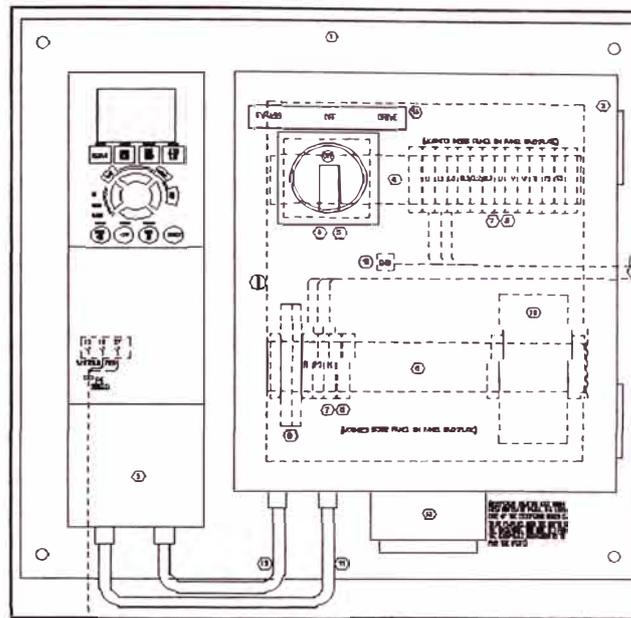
Placa de montaje con variador para control del Conveyor.
